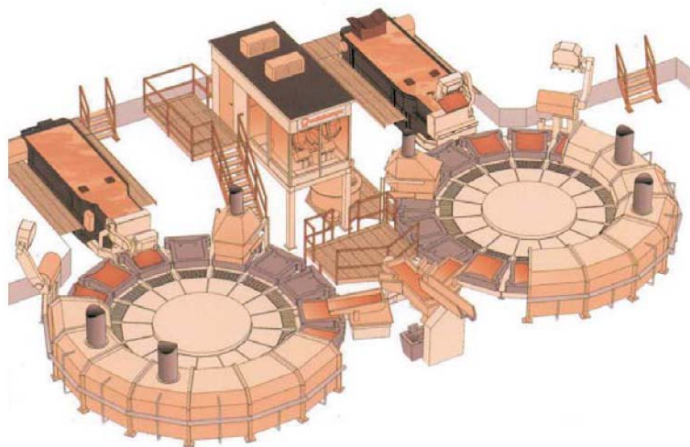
Принципова схема ливарної машини з двома ливарними колесами [16]
